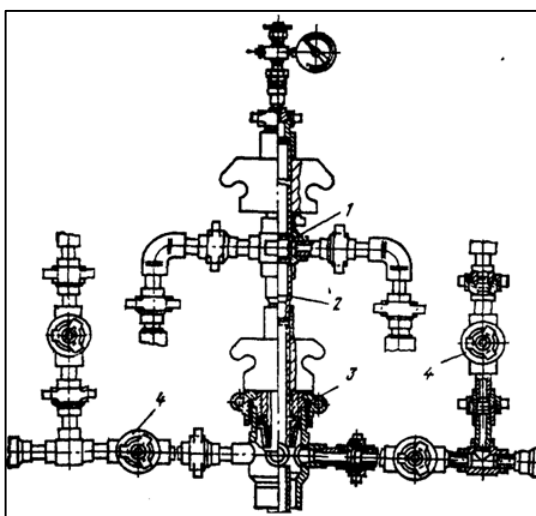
Арматура 2АУ-700: 1 - трубная головка (крестовина); 2 - патрубок; 3 - устьевая головка с сальником; 4 - пробковый кран
